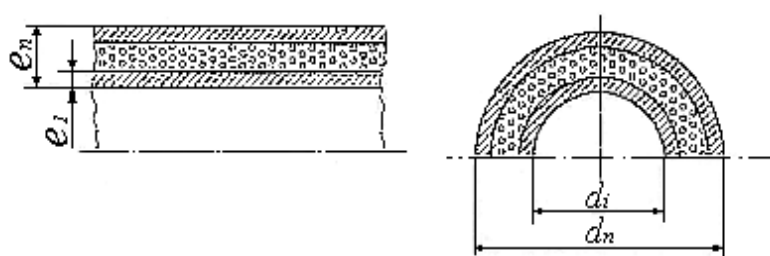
Продольный и поперечное сечение труб типа А (без раструба) и гладкой части труб раструбных типа А
